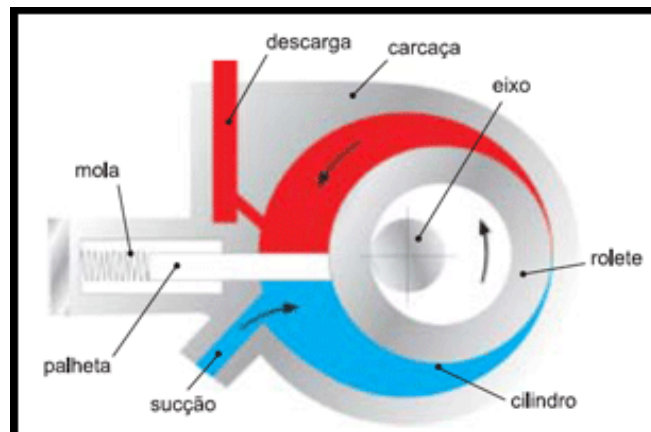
Desenho Esquemático de um compressor rotativo
